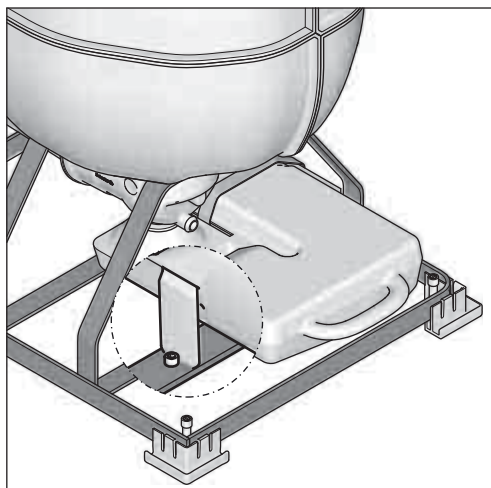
Far scattare in posizione la linguetta stabilizzante
